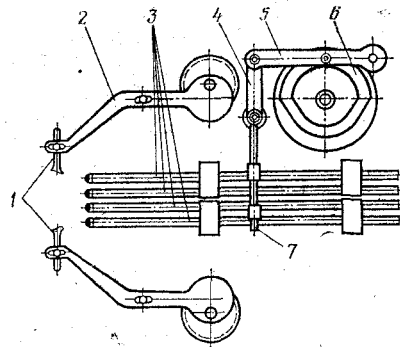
Схема щеточного устройства для отбора нитей с цен
